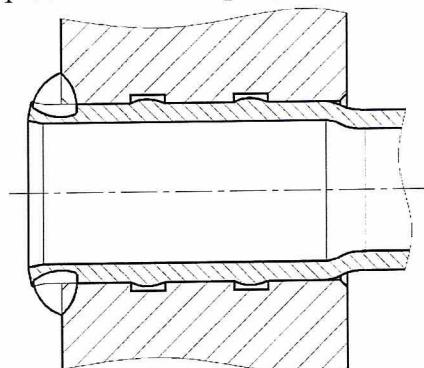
Развальцовка трубы за сварным швом.
